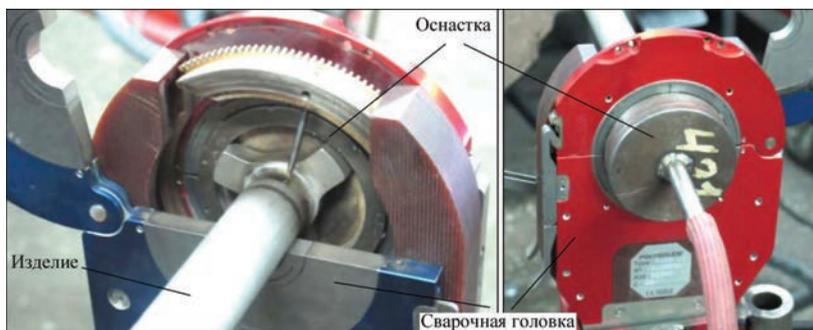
Крепление сварочной головки закрытого типа на специальную оснастку
